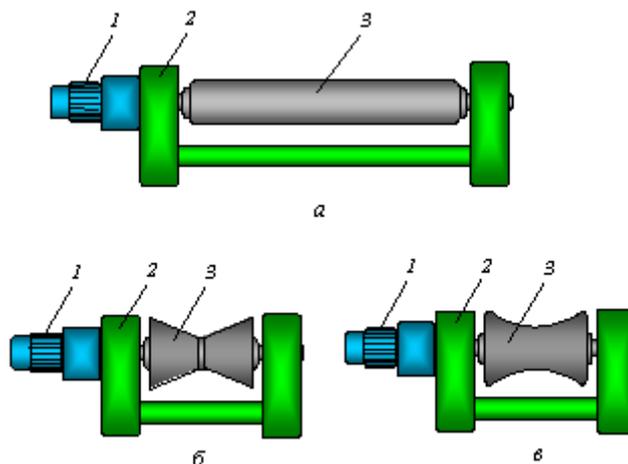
Рольганги с индивидуальным приводом и роликами: *а* — цилиндрическим; *б* — биконическим; *в* — профильным; *1* — мотор-редуктор; *2* — подшипниковая опора; *3* — ролик
